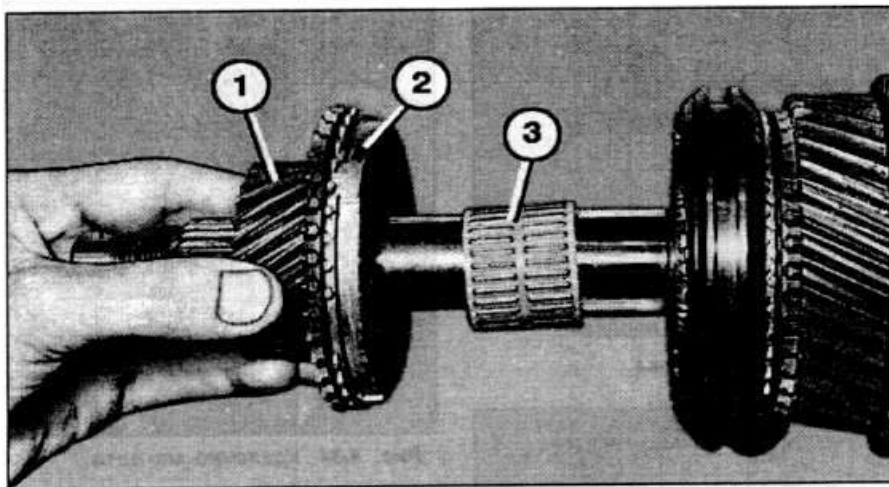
Снятие со вторичного вала шестерни V передачи 1 кольца синхронизатора 2 и игольчатого подшипника 3
